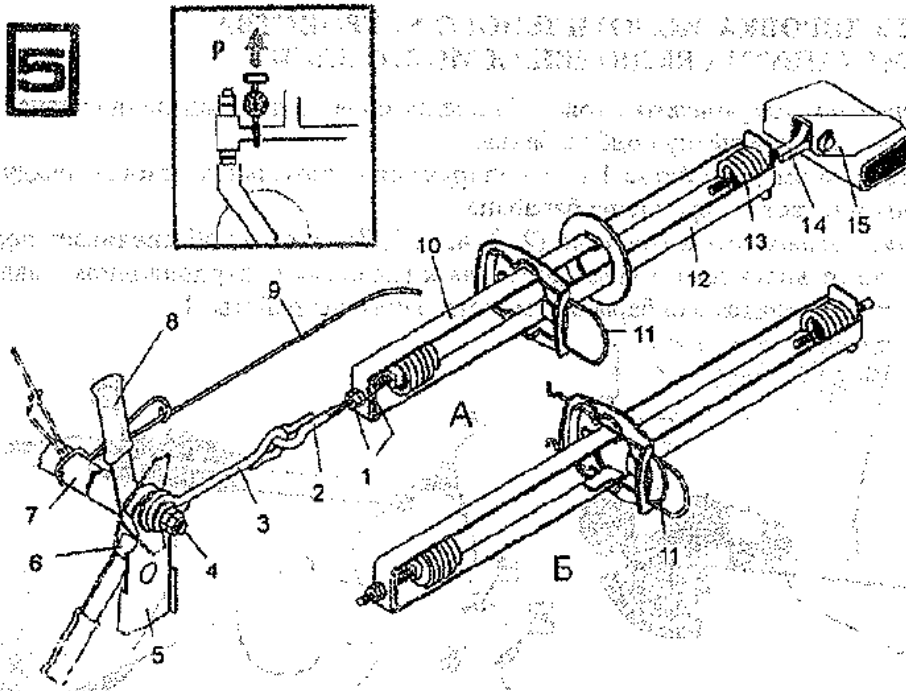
Разгружающее устройство: А - установка разгружающего устройства; Б - транспортное положение фиксатора (рабочее его положение изображено штрихпунктирными линиями); 1 - гайка регулировочная; 2 - растяжка; 3 - шпренгель; 4 - цапфа эксцентриковая; 5 - стойка; 6 - упор; 7 - балка нормализатора; 8 - рычаг; 9 - палец; 10, 12 - обоймы; 11 - фиксатор; 13 - пружина растяжения; 14 - растяжка; 15 - балка платформы
